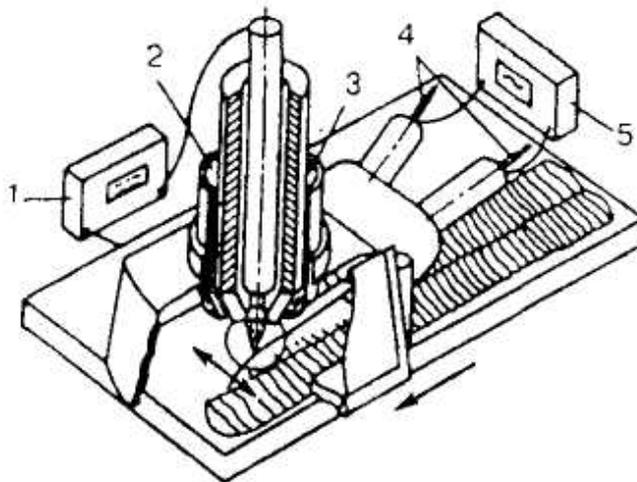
Схема устройства для плазменной наплавки горячей проволокой: 1 – источник питания; 2 и 3 – полости для подачи защитного и плазмообразующего газов; 4 – наплавочные проволоки; 5 – источник подогрева проволок
